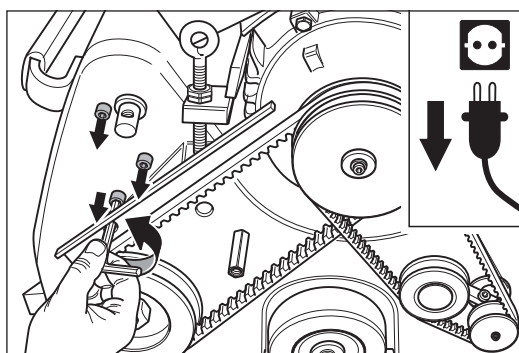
Das Aggregat festhalten und gleichzeitig die drei Befestigungsschrauben des Aggregats entfernen.
